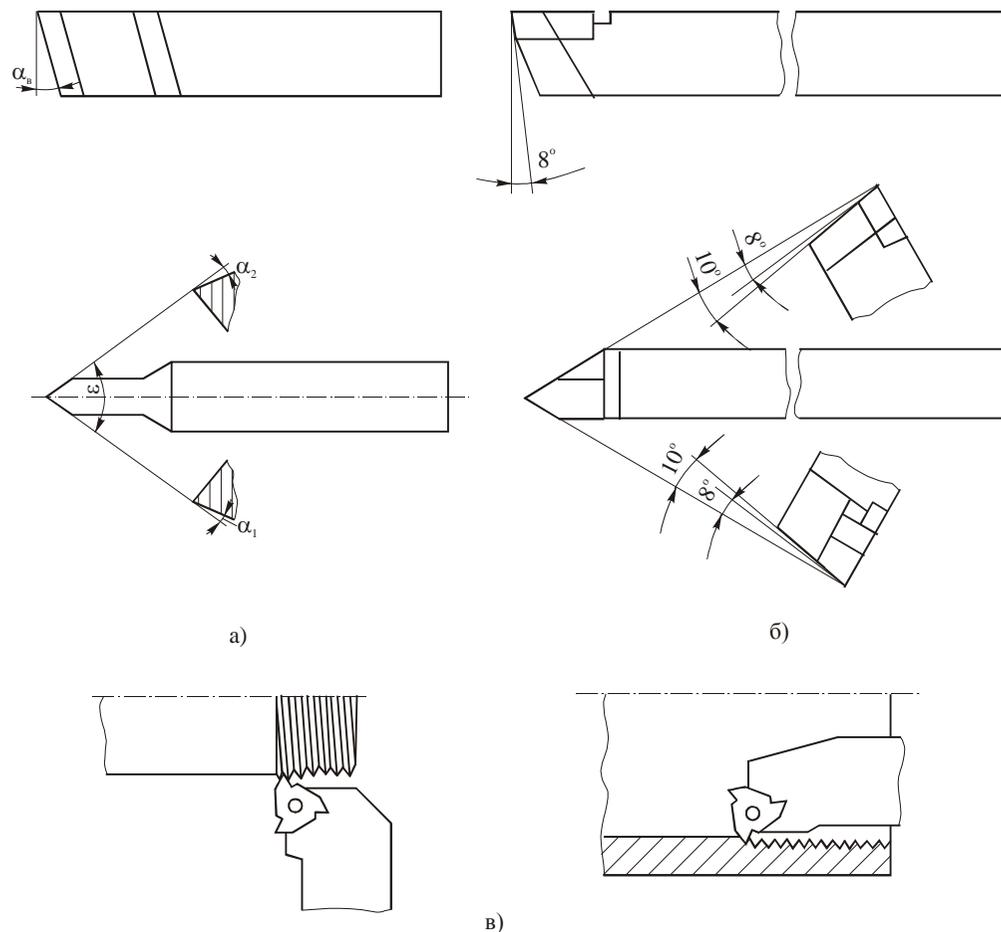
Типы стержневых резьбовых резцов: *а* – из быстрорежущей стали; *б* – с напайной твердосплавной пластиной; *в* – с механическим креплением твердосплавной пластины
